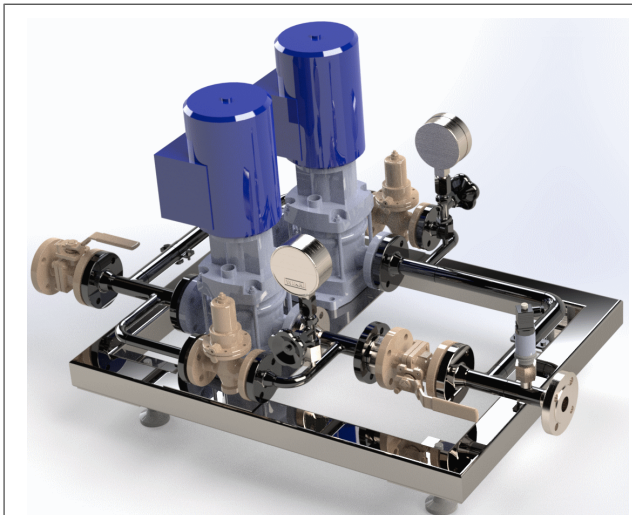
Ausführung Pumpenbaugruppe Typ 7111-2
